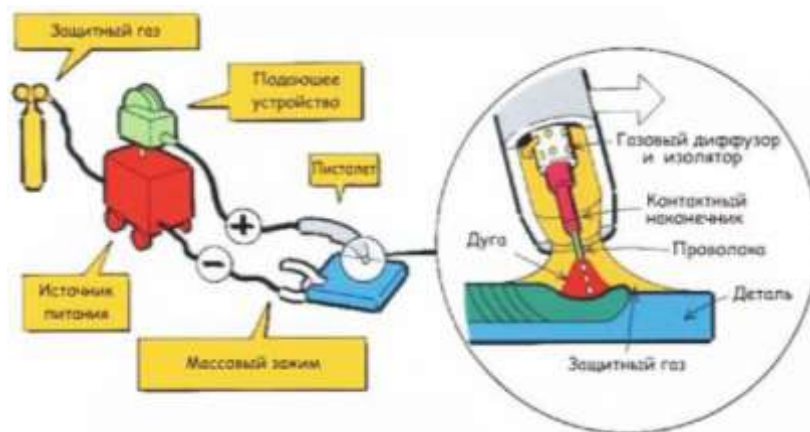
Схема сварки в среде инертного газа
